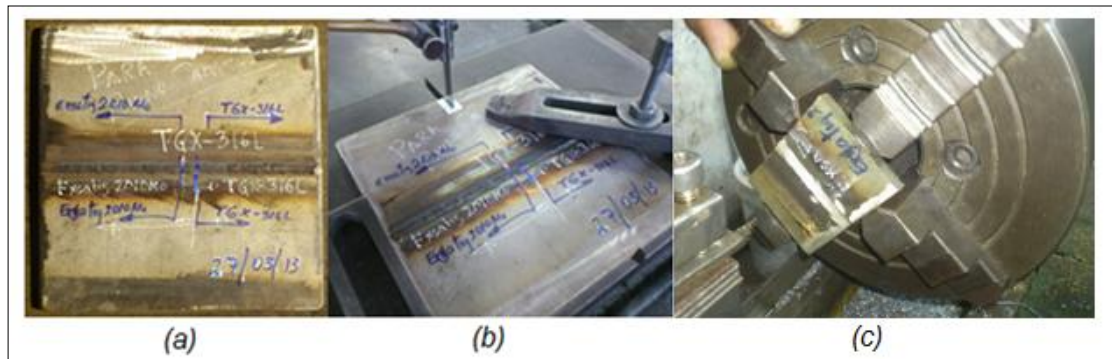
(a) plancha antes de maquinar. (b) corte en máquina herramienta. (c) obtención de pastillas de 15 mm de diámetro en torno.
